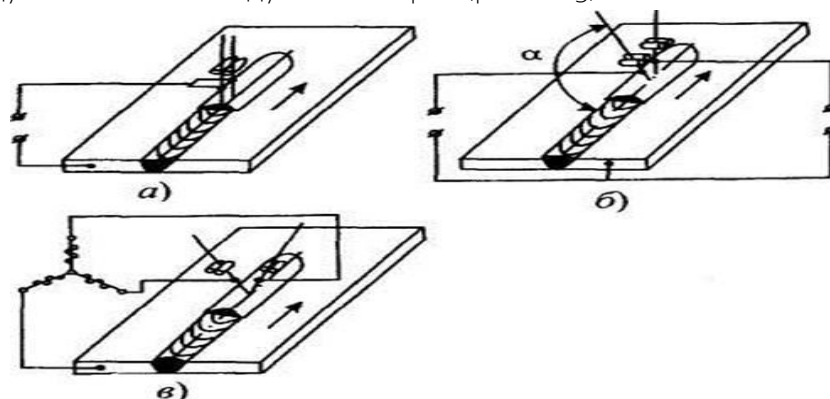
Схемы образования шва при сварке: а - сдвоенным электродом; б - двухдуговой; в - трехфазной дуговой
